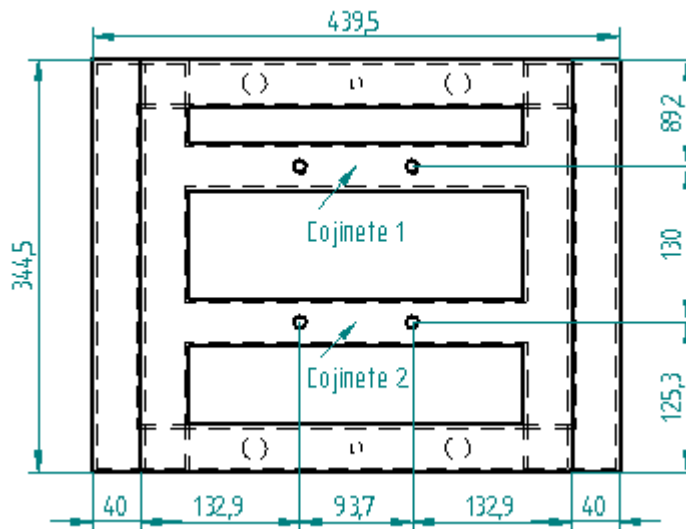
Colocación de cojinetes en la estructura (vista de planta).
